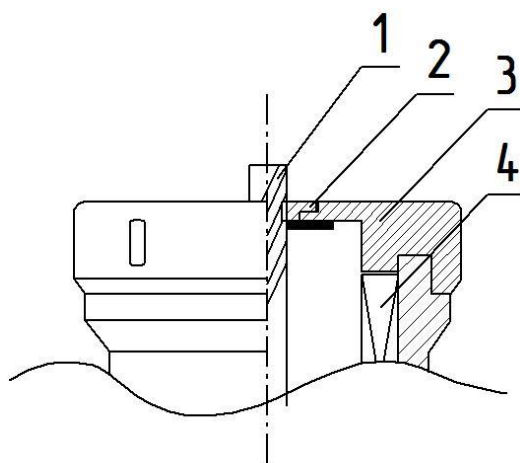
Конструкция поворотного механизма ЛЭМД
